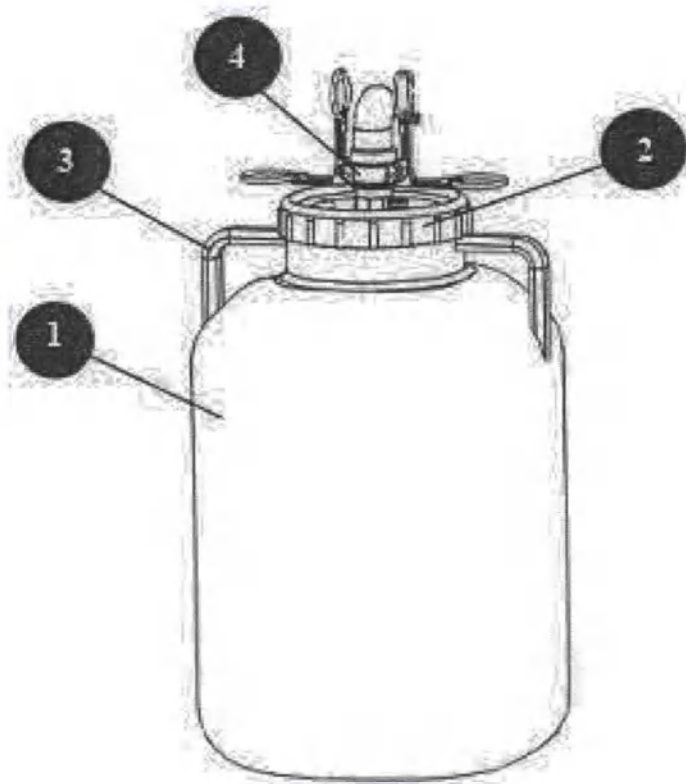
Устройство бака для сбора медицинских отходов класса «Г», где 1 – Корпус бака для сбора медицинских отходов класса «Г»; 2 – Крышка корпуса бака для сбора медицинских отходов класса «Г»; 3 – Ручка бака для сбора медицинских отходов класса «Г»; 4 – Соединение, оснащенное системой CAMLOCK
